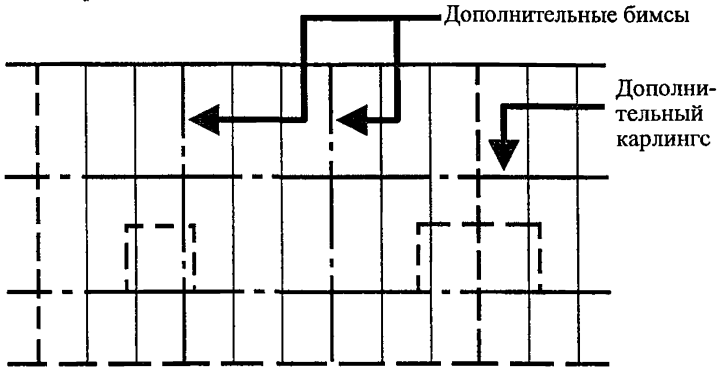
Вариант подкрепления палубного перекрытия дополнительными рамными карлингсом и бимсами
